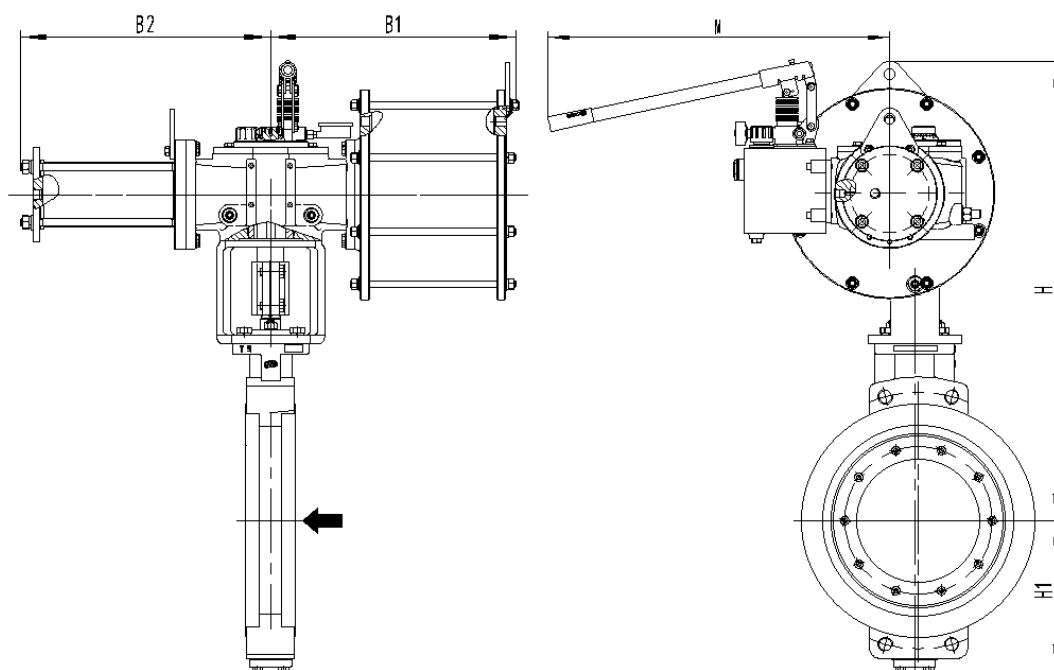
AW40D004~AW90D007 带液压手轮外形尺寸图
